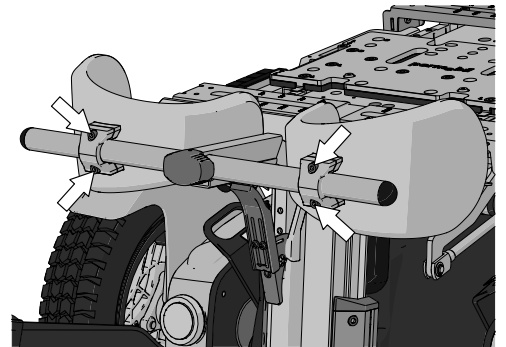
An jeder Halterung sind zwei Schrauben.
